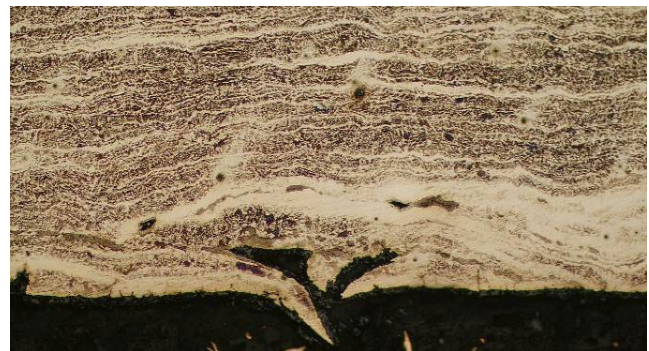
Сталеплавильные пленки и вздутия по раскатанным дефектам макроструктуры непрерывнолитой заготовки на внутренней поверхности трубы:
